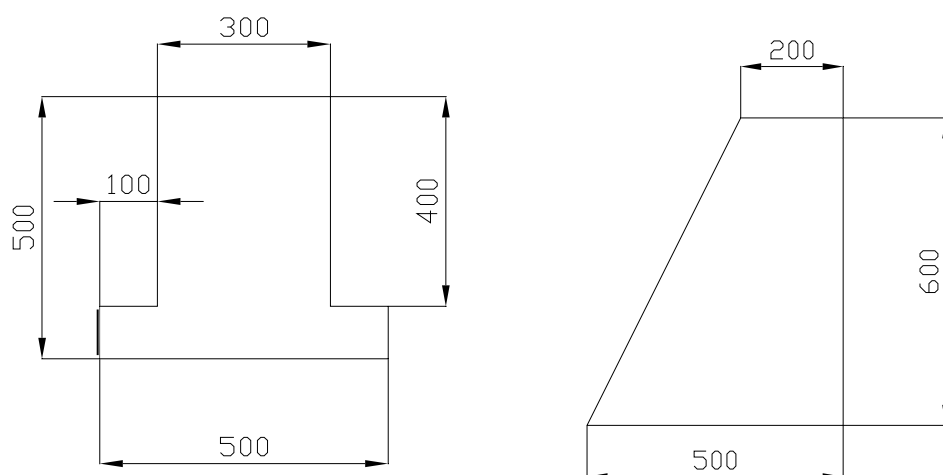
Размеры контура привода револьверной головки, суппорта и задней бабки станка
